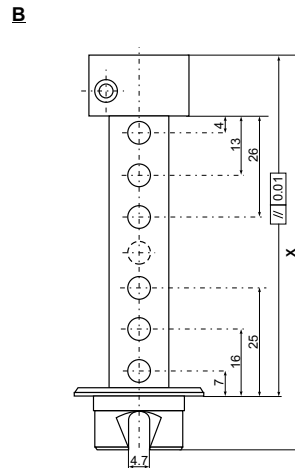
Technische Zeichnung der Platte-Platte-Geometrie mit einem Durchmesser von 15 mm.
